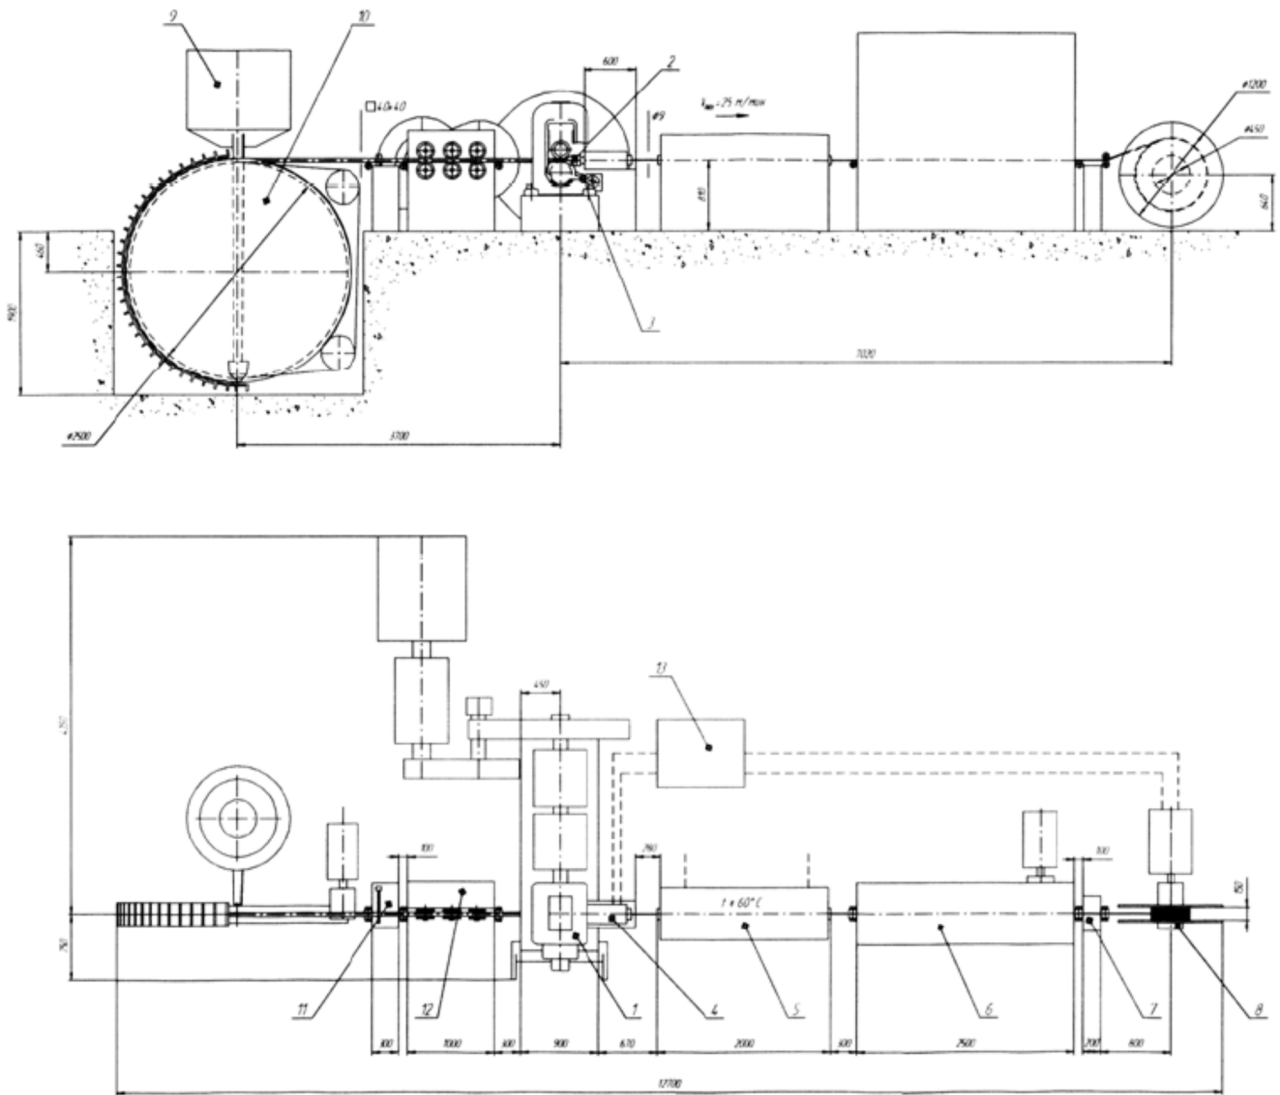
Принципова схема лінії безперервної обробки алюмінію і його сплавів
